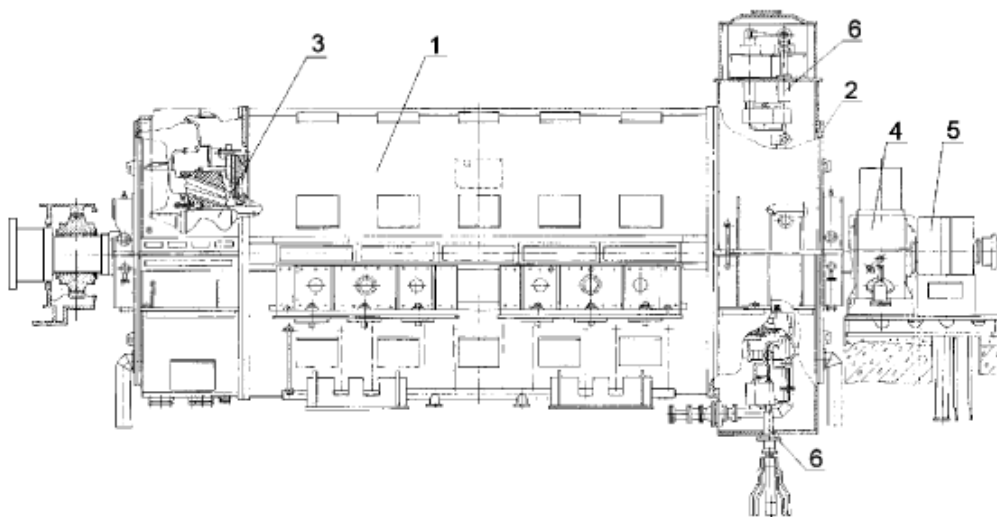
Общая схема турбогенератора ТЗВ: 1 — статор; 2 — щит наружный с напорной и сливной камерами; 3 — ротор; 4 — подшипник; 5 — аппарат щеточно-контактный; 6 — вывод концевой
